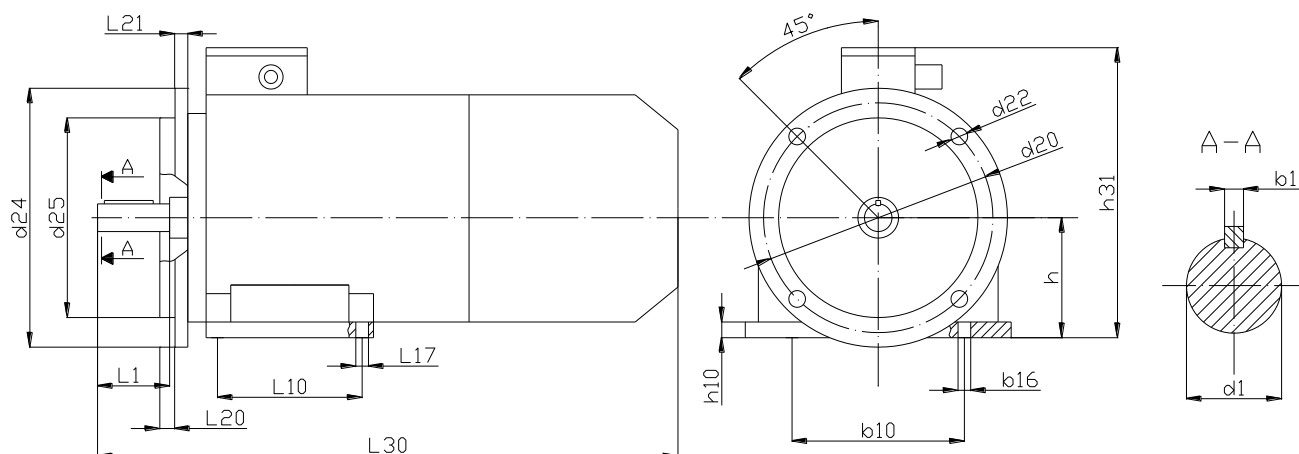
Габаритные и установочно-присоединительные размеры
